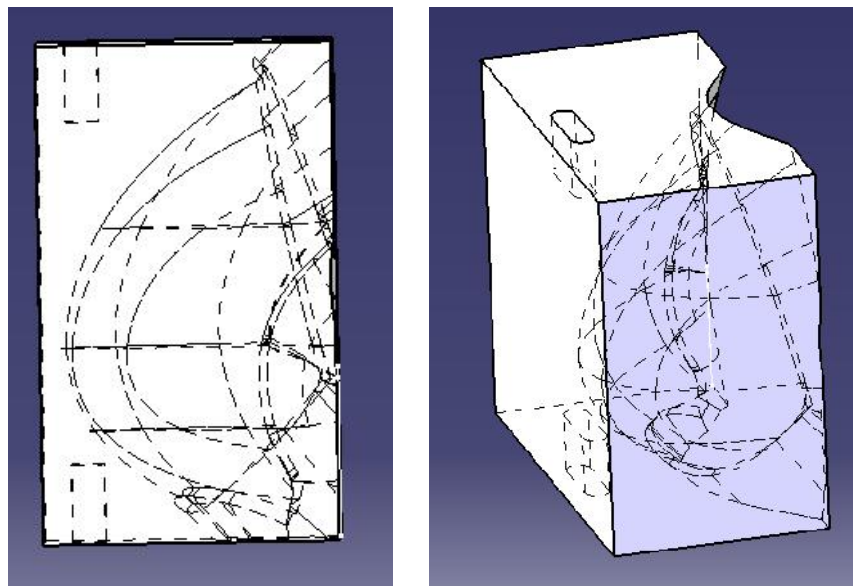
CAD del molde hembra definitivo
